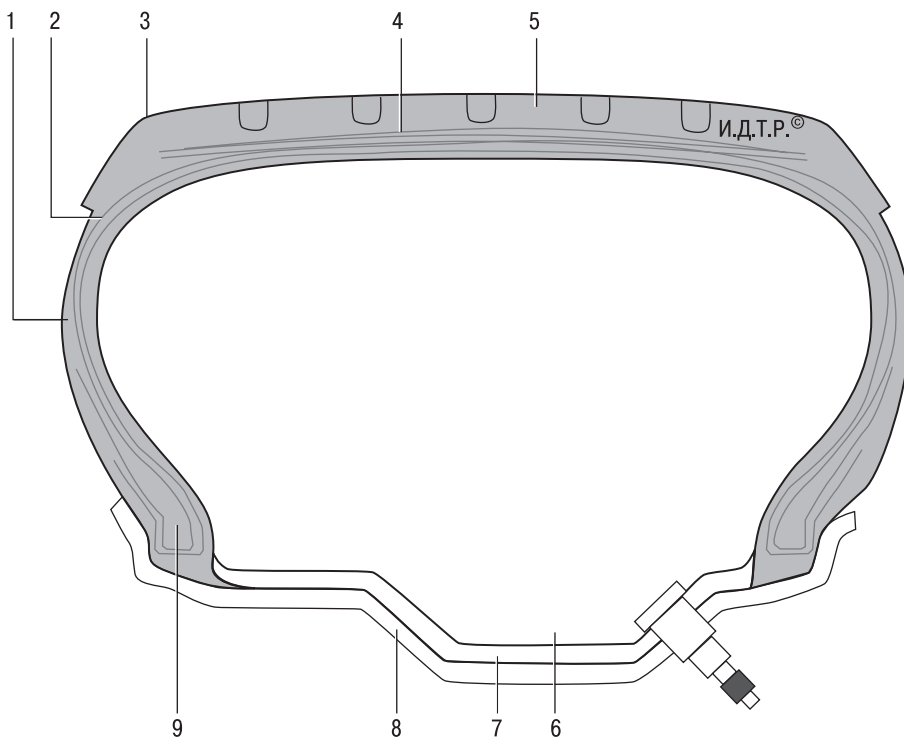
Элементы конструкции шины: 1 – боковина; 2 – каркас; 3 – плечевая зона; 4 – брекер; 5 – протектор; 6 – камера; 7 – ободная лента; 8 – обод колеса; 9 – борт
